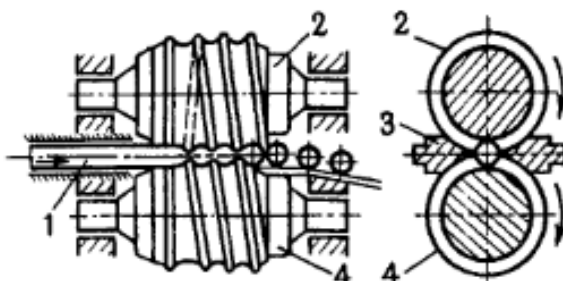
Схема прокатки шаров в стане поперечно-винтовой прокатки [2]
